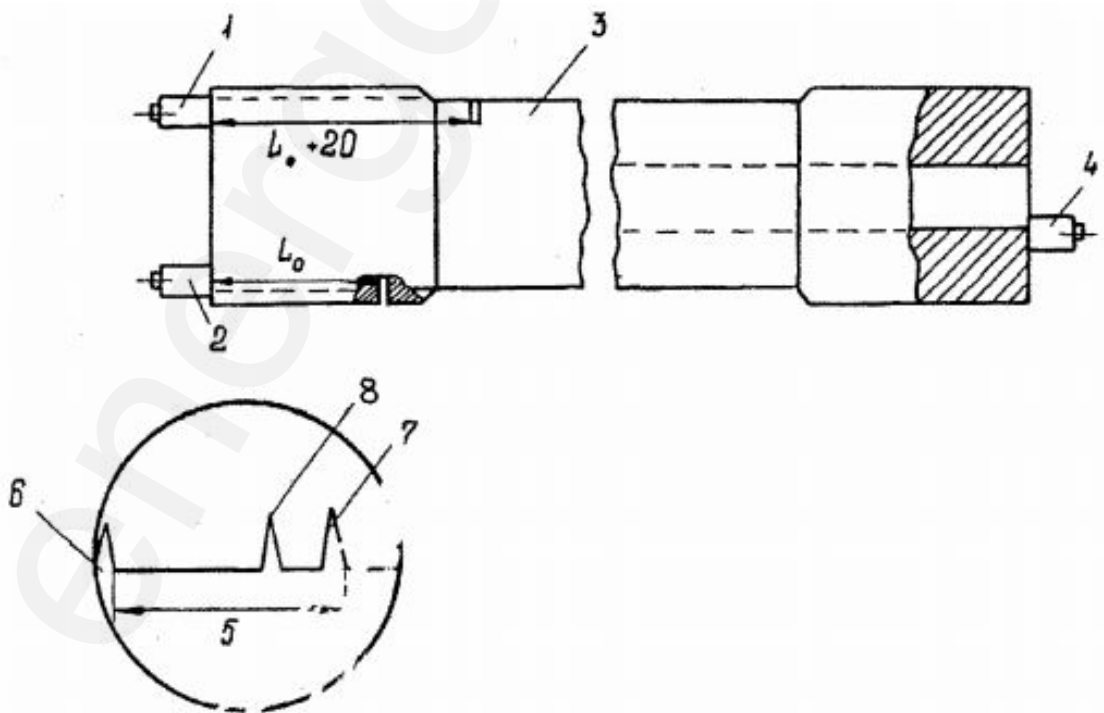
Схема настройки скорости развертки и чувствительности дефектоскопа при контроле резьбовых участков шпильки:
